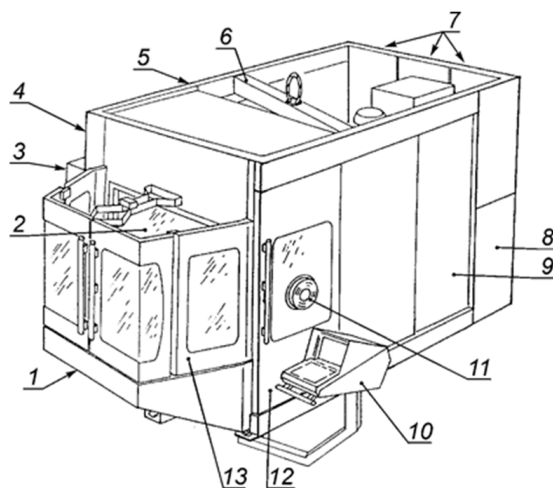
Общий вид обрабатывающего центра с горизонтальным шпинделем и маятниковым устройством смены инструмента:
